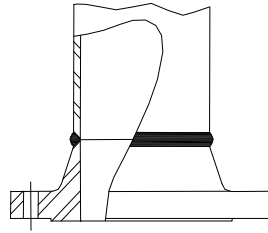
Cuello soldable (Welding Neck).
